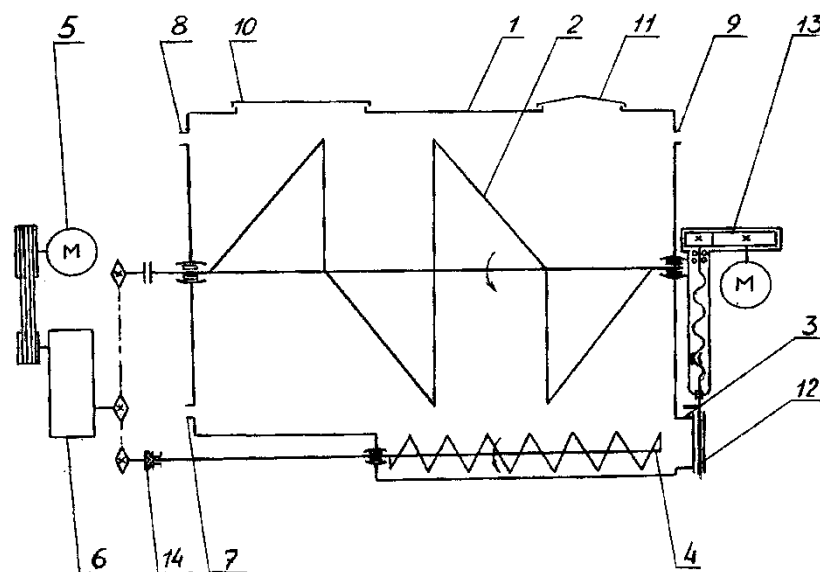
Змішувач кормів одновальний СКО-Ф-6: 1–корпус; 2–мішалка; 3–вивантажувальна горловина; 4 – вивантажувальний шнек; 5 – електродвигун; 6 – редуктор; 7 – паровий колектор; 8 – патрубок; 9 – зрошувачі; 10 – завантажувальний люк; 11 – кришка; 12 – заслінка; 13 – мотор-редуктор; 14 – муфта кулачкова.
